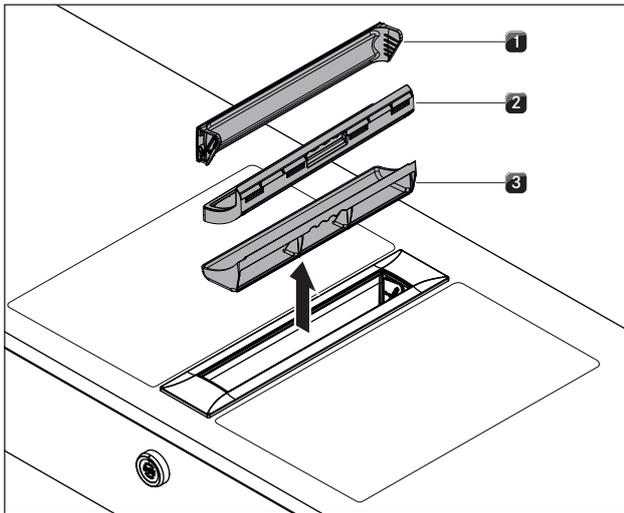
Desmontaje de los componentes del filtro de grasa
